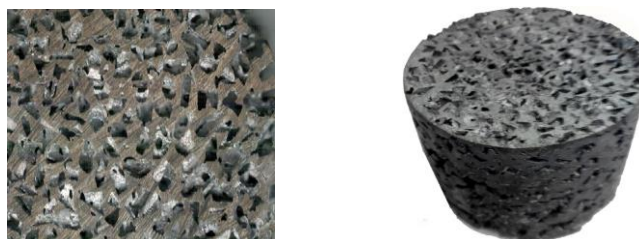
Пористая заготовка-преформа из матричного алюминиевого сплава для пропитки легкоплавким наполнителем
